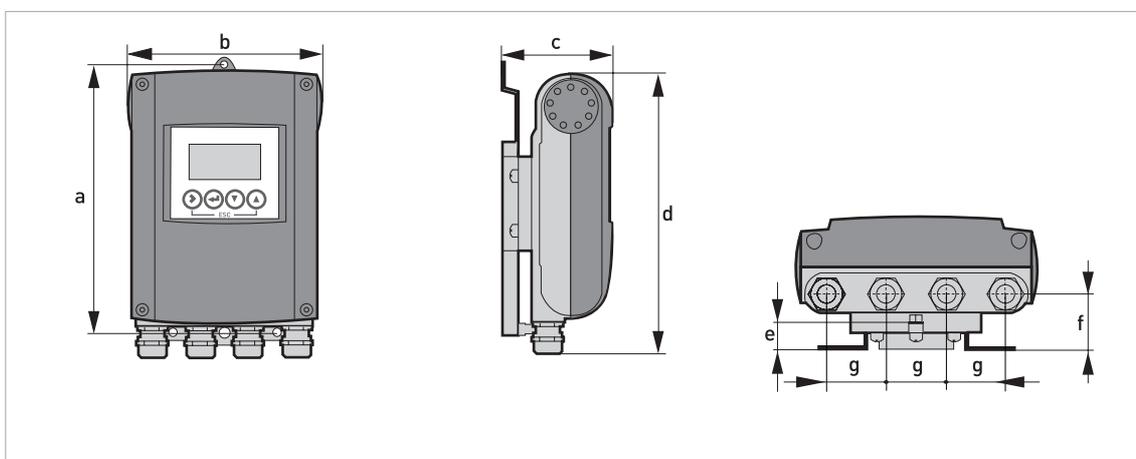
Dimensions de la version pour montage mural, boîtier en aluminium
